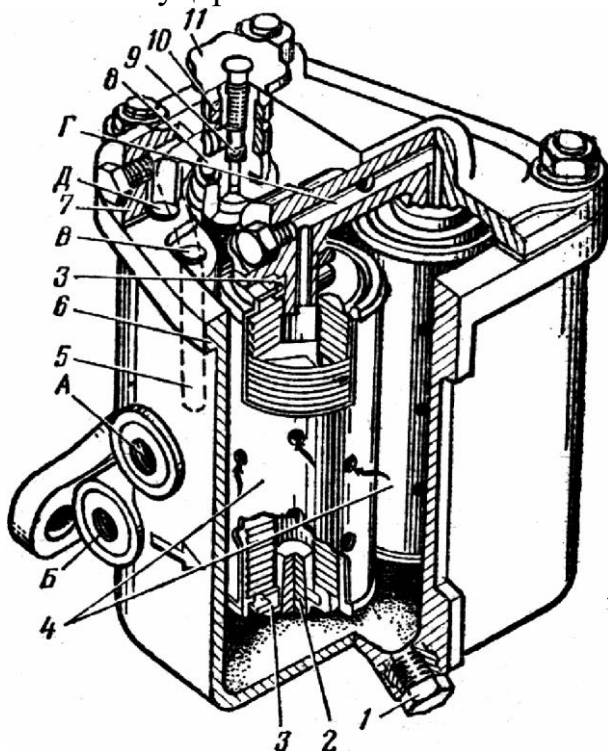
Фильтр тонкой очистки топлива двигателя Д-240:
